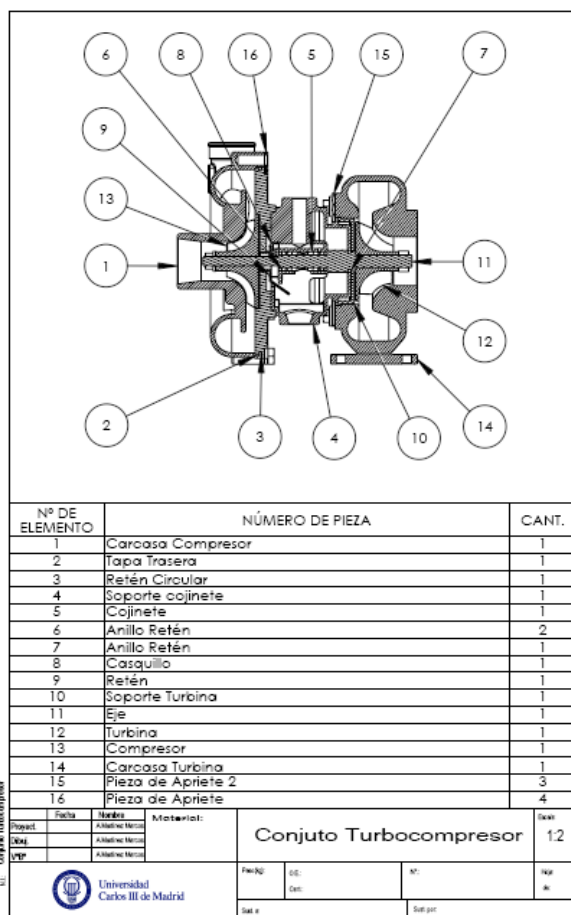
Imagen del Plano de Conjunto del Turbocompresor
